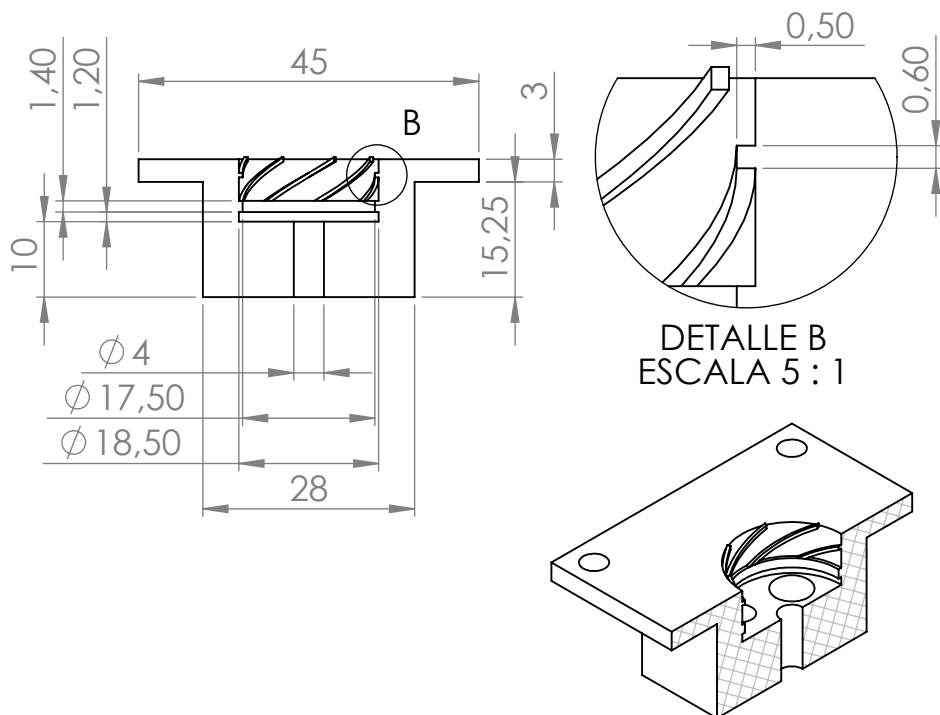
Vista en corte del molde del *Robot Rotator* parte B
